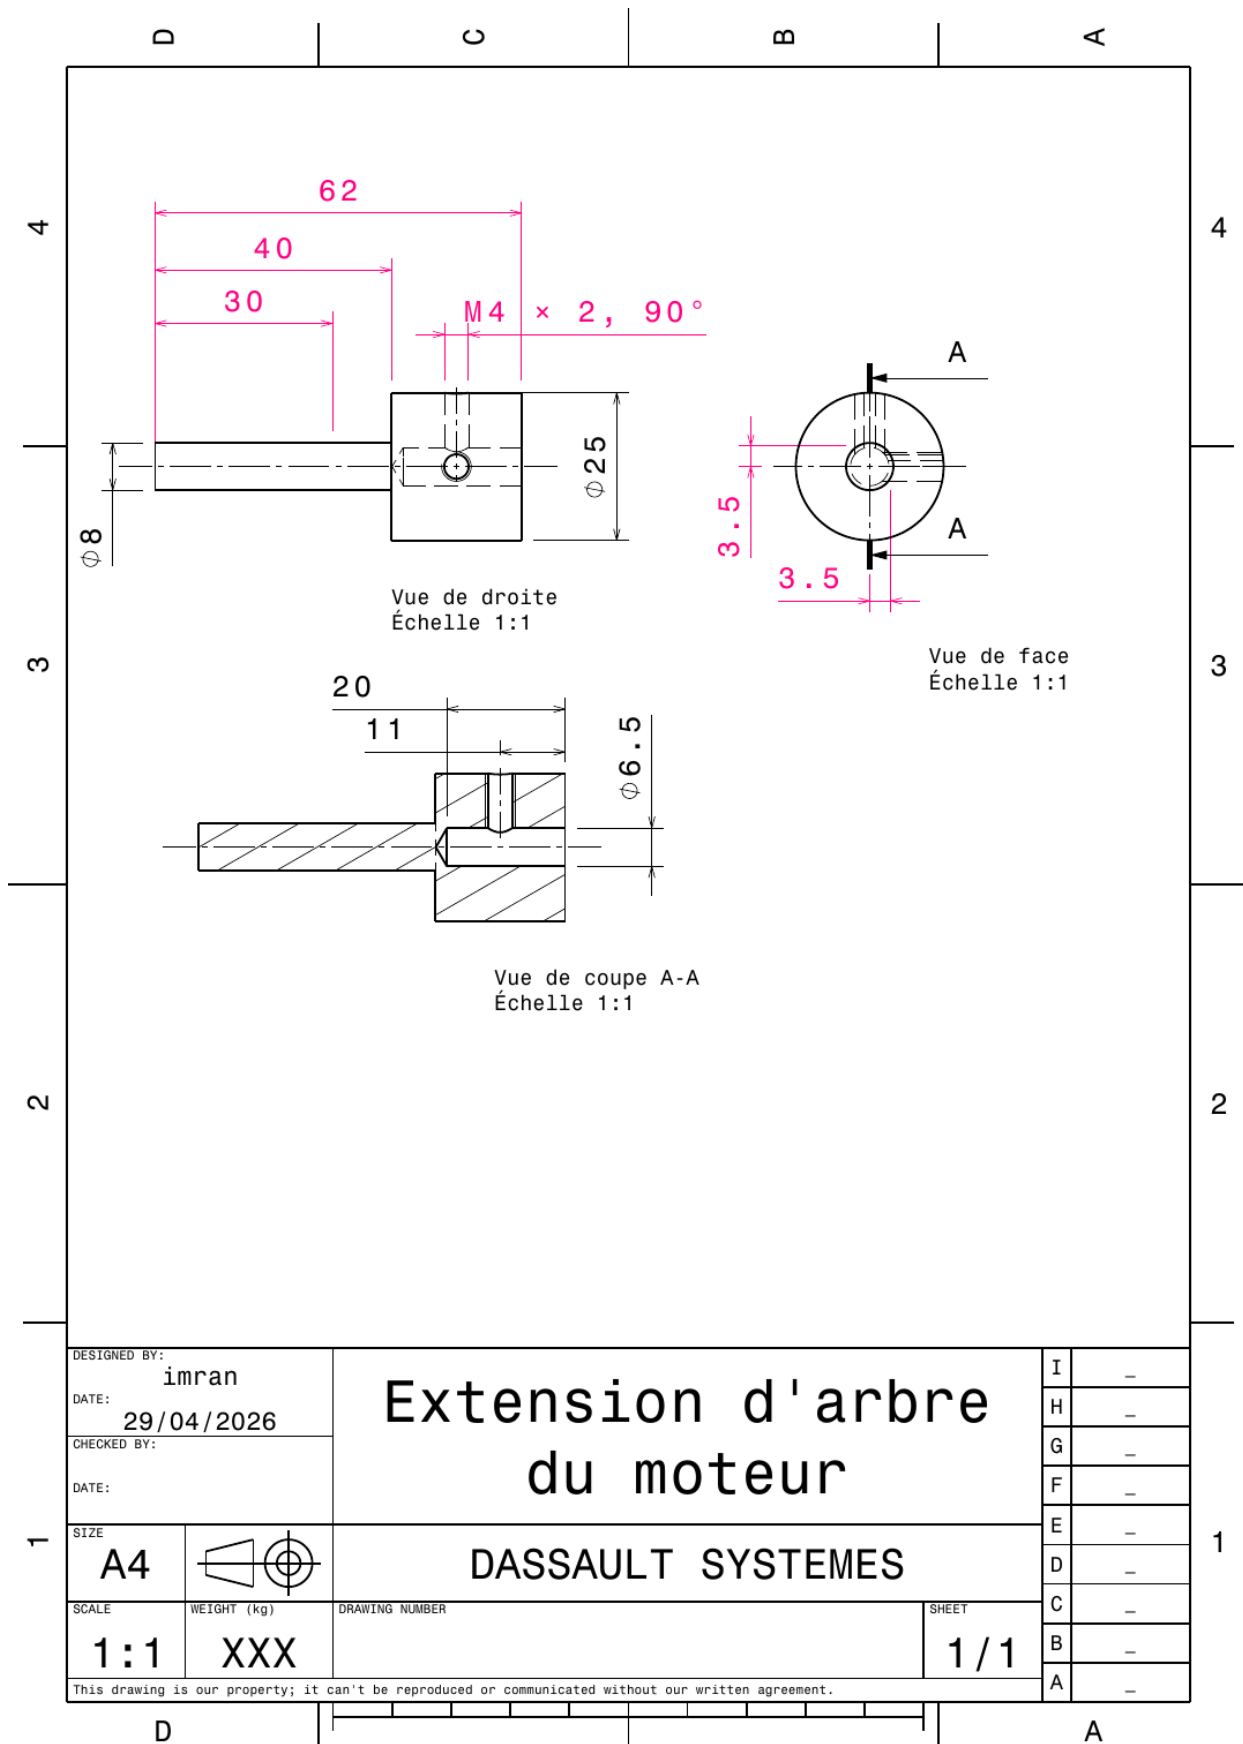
Dessin de définition — Extension d'arbre du moteur.
